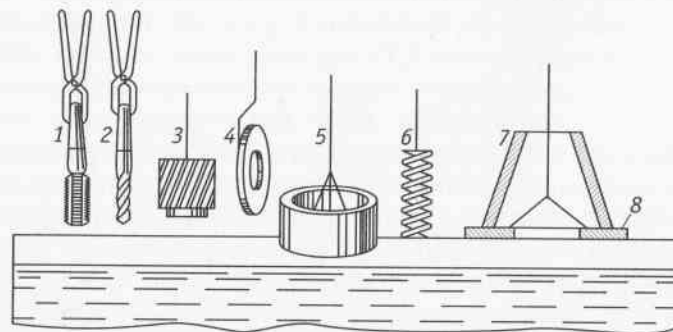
Погружение деталей в закалочную среду с учетом их формы: 1 — метчик; 2 — сверло; 3 — фреза; 4 — диск; 5 — кольцо; 6 — пружина; 7 — деталь с тонкими стенками; 8 — приспособление
